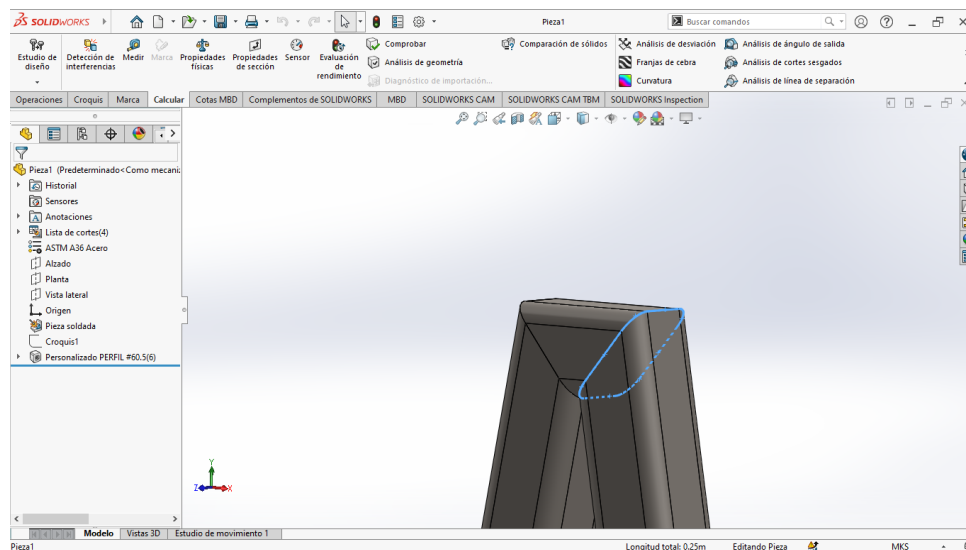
Soldadura en la estructura - perfil #60.5, material acero A-36. Fuente: Autor
